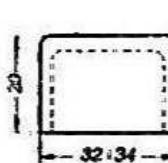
Размеры выпускного окна двигателя 123 см³:
